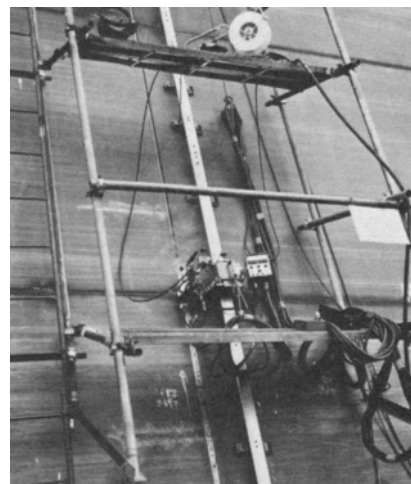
エレクトロガス溶接（造船の溶接—35年の歩み）
